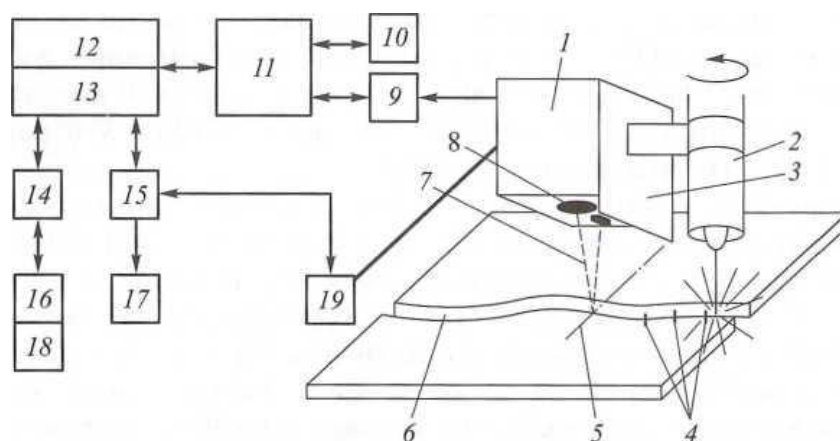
Система дуговой сварки роботом с СТЗ: 1 – видеосенсор; 2 – сварочная головка; 3 – щиток; 4 – позиции коррекции; 5 – линия сканирования; 6 – стык; 7 – лазерный луч; 8 – телекамера; 9 – специализированный процессор; 10 – процессор обработки изображения (ПОИ); 11 – шина; 12 – интерфейс микроЭВМ; 13 – супервизорное устройство управления; 14 – интерфейс сварочного стола; 15 – устройство управления роботом (УУР); 16 – контроллер сварочного стола; 17 – сварочное оборудование (СО); 18 – сварочный стол; 19 – робот
